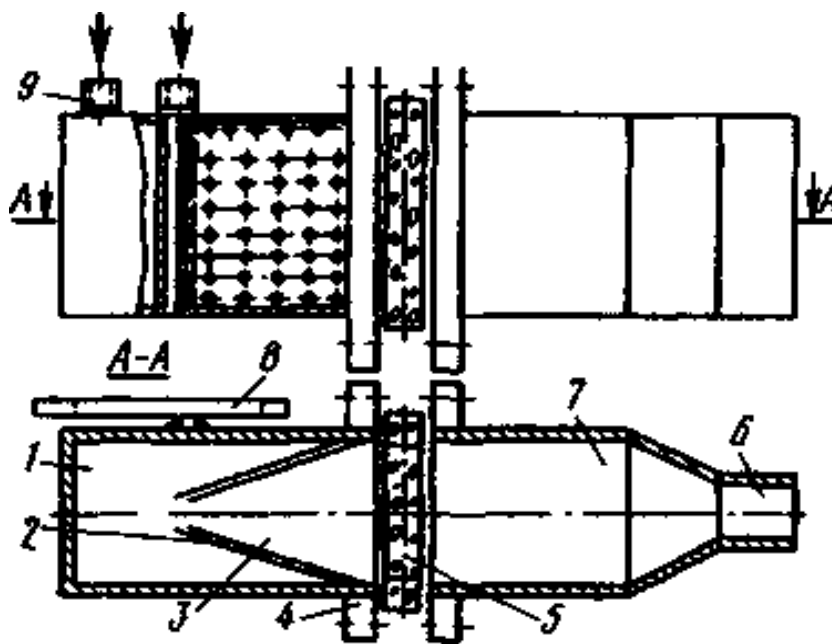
Схема газового пальника для обробки свинячих голів:
